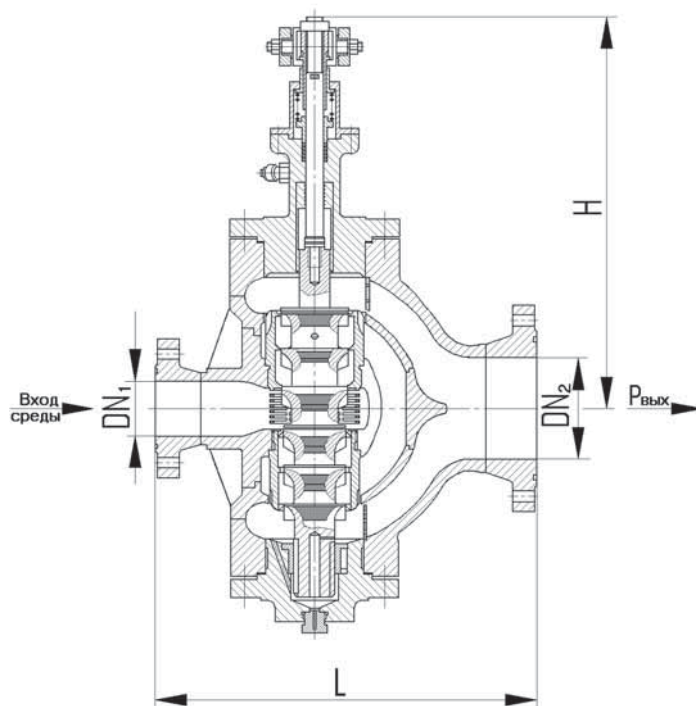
Клапан регулирующий проходной с гидроприводом
